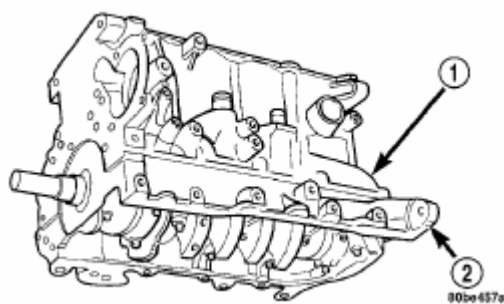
Блок цилиндров с крышкой коренных подшипников.
